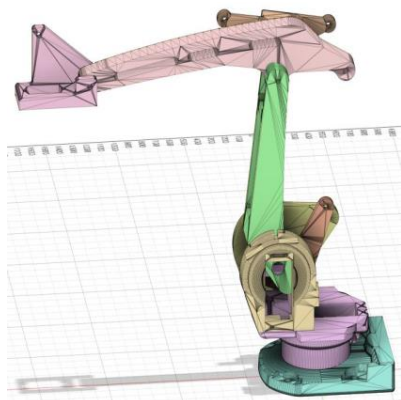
Ensamble final de los elementos 3D diseñados.
